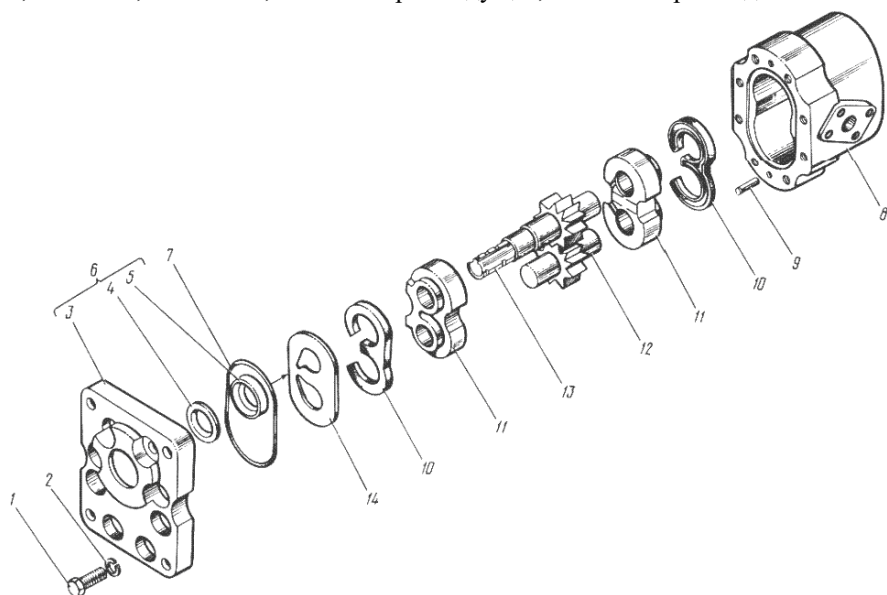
Насос НШ10 в разобранном виде: 1 - болт; 2 -шайба; 3 - крышка передняя; 4 - кольцо опорное; 5 – манжета; 6 - крышка передняя в сборе; 7 - кольцо уплотнительное; 8 – корпус; 9 – штифт; 10 – манжета фигурная; 11 – подшипник; 8 – кольцо опорное; 10 – пластина; 11 – канал; 12 – шестерня ведомая; 13 - шестерня ведущая; 14 –пластина.
